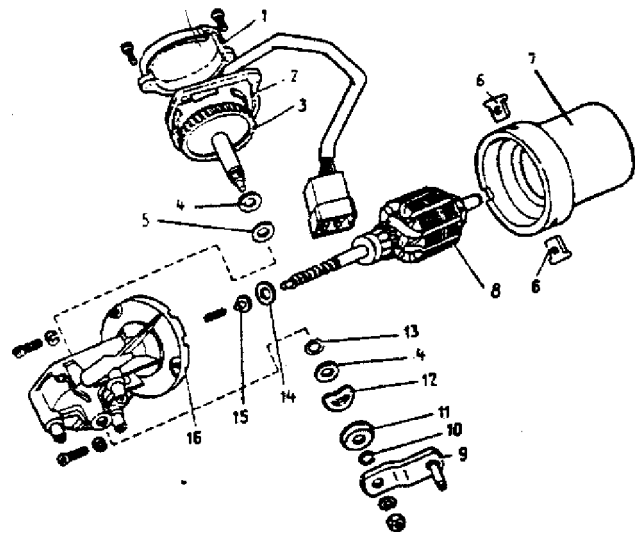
Componentes do motor elétrico do limpador do pára-brisa: 1 - tampa; 2 - placa; 3 - engrenagem redutora; 4 - arruela de aço; 5 - arruela sintética; 6 - presilhas de fixação dos parafusos; 7 - carcaça; 8 - induzido; 9 - manivela; 10 - anel de retenção; 11 - capa de proteção; 12 - arruela elástica; 13 - anel de vedação; 14 - arruela de ajuste; 15 - centralizador; 16 - tampa.
